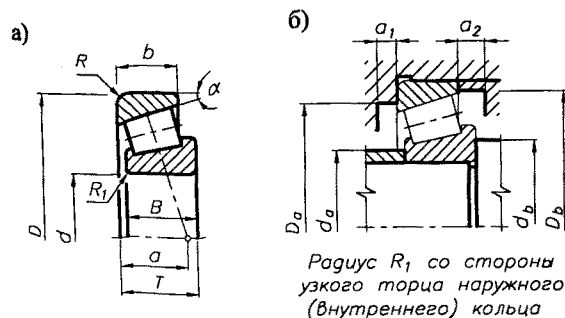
Габаритные и установочные размеры роликовых конических однорядных подшипников
